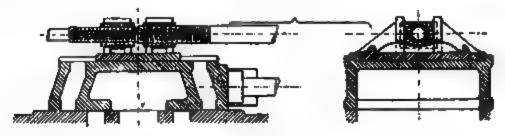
Meyersche Steuerung mit veränderlicher Expansion, gewöhnlich während des Ganges von Hand verstellbar.
